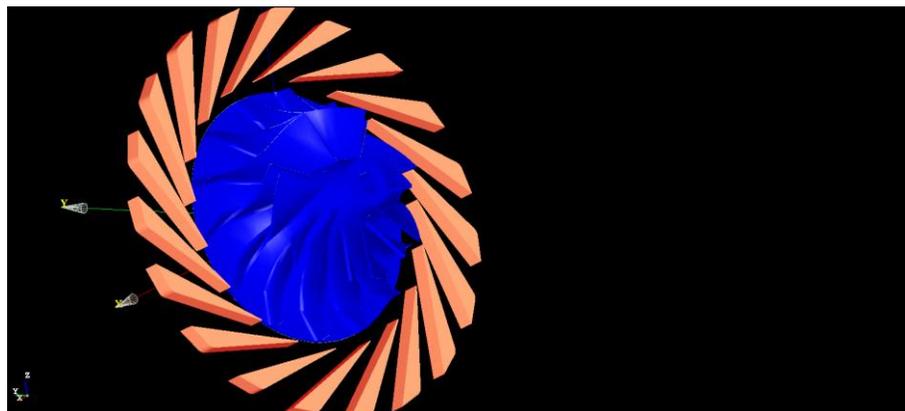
Крыльчатка и лопатки диффузора компрессора
